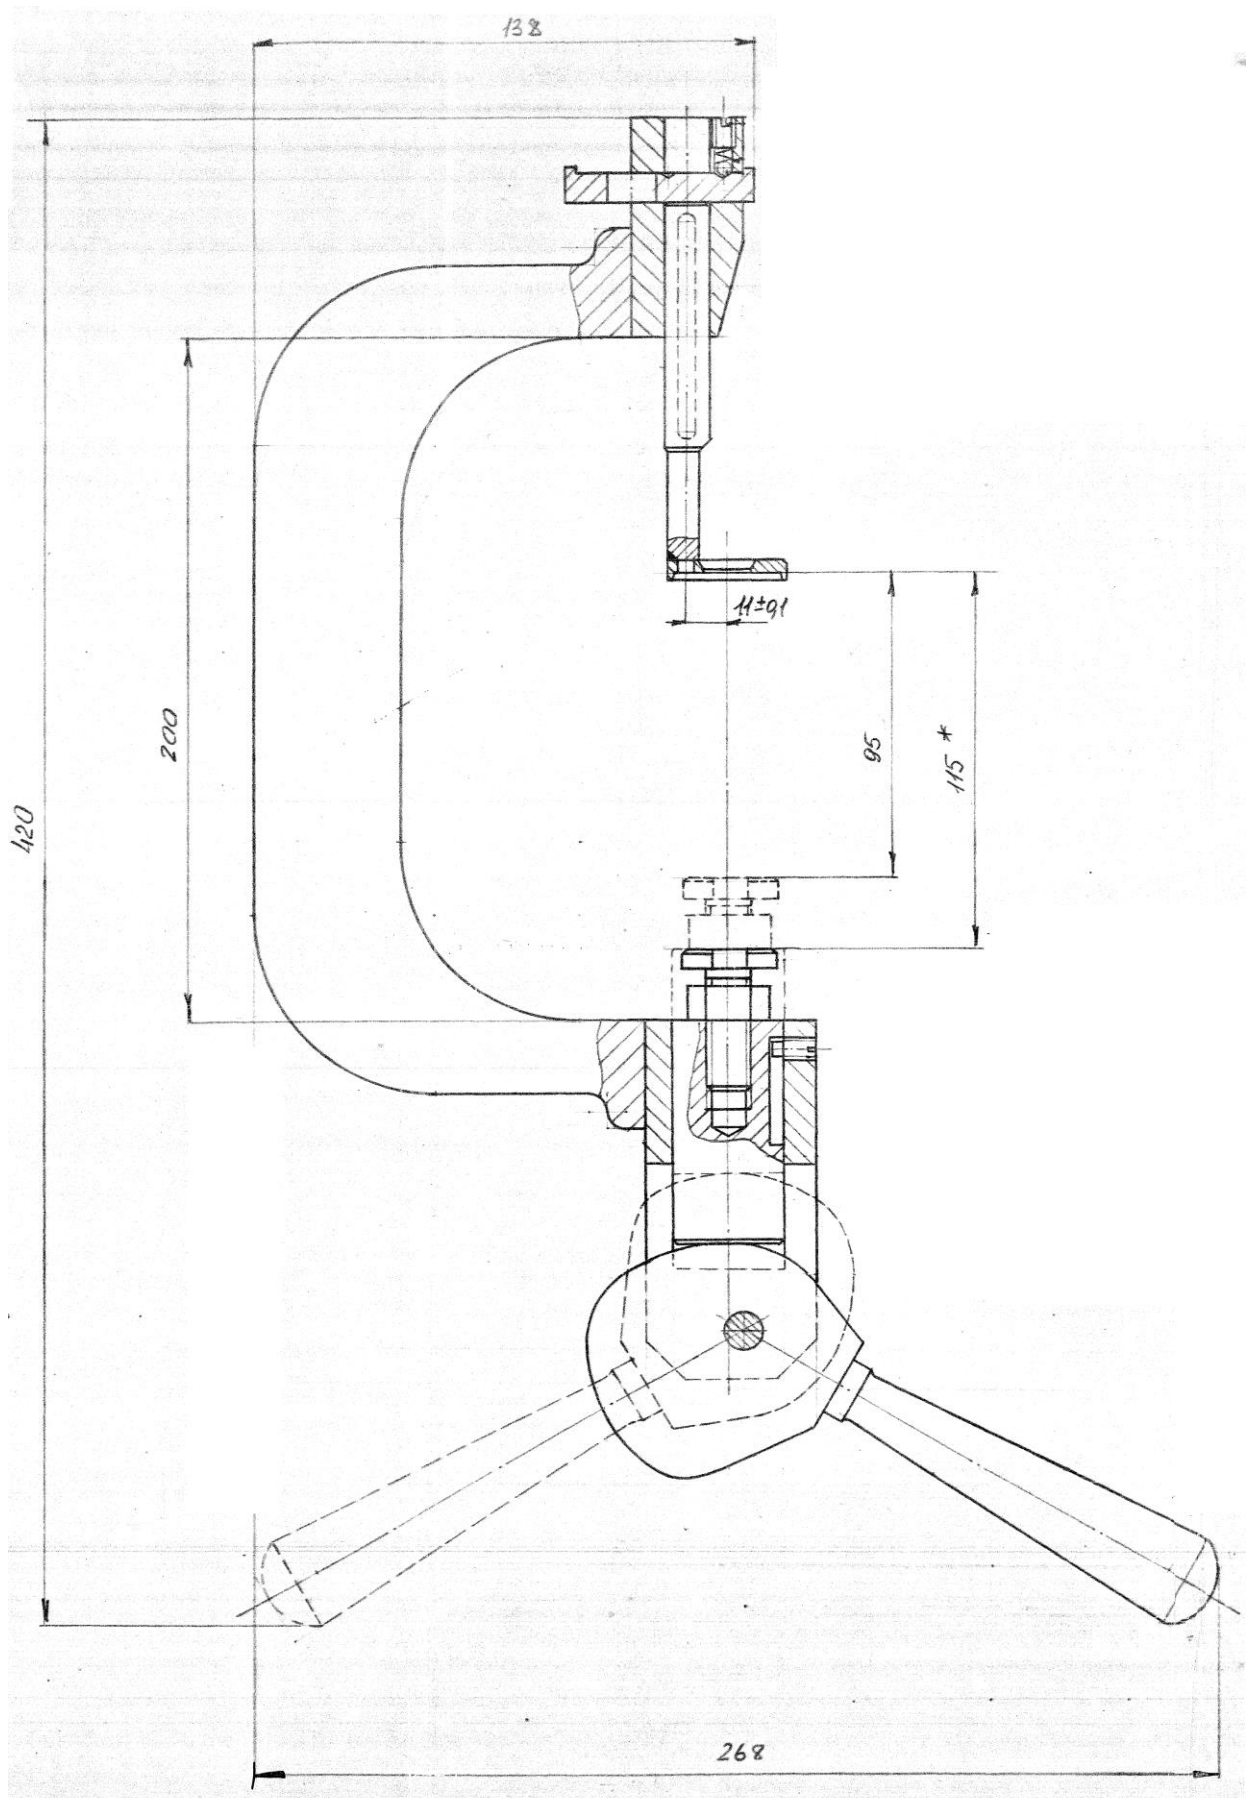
ЗМ 7814-5119 – Приспособление для засушивания и рассушивания клапанов
